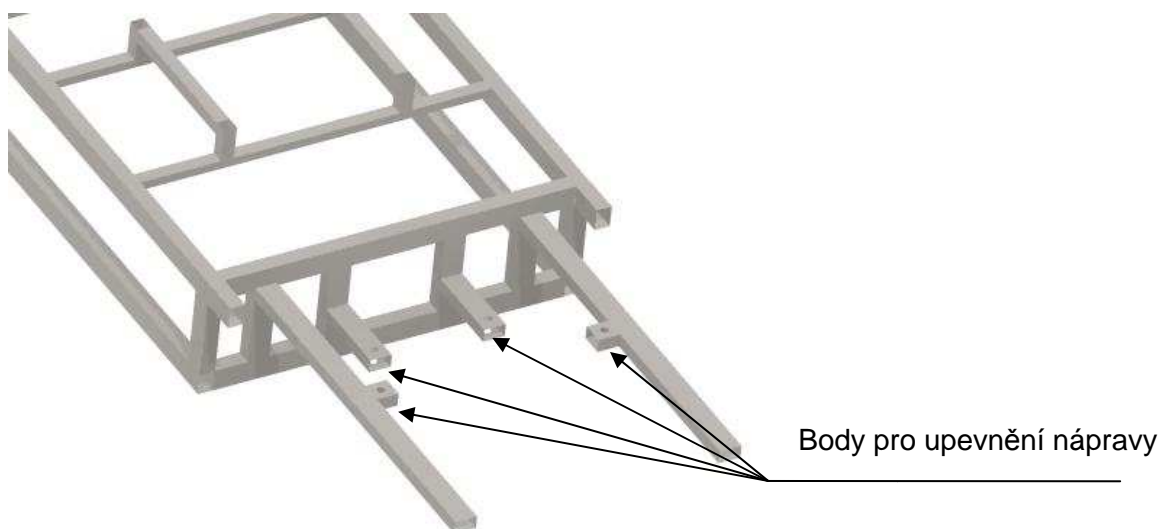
Detailní pohled rámu s držáky pro uchycení ramen zadní nápravy
